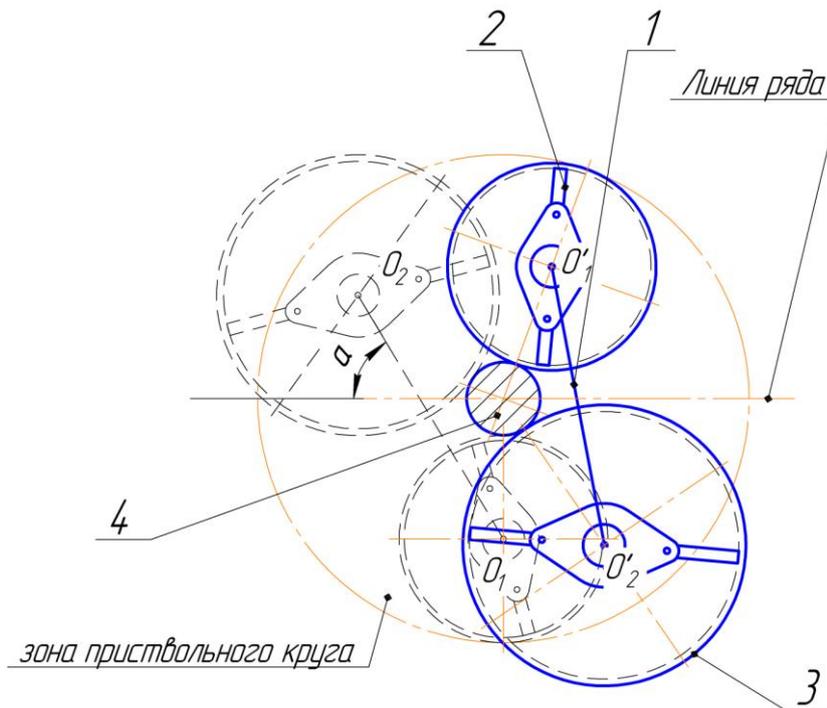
Конструктивная и технологическая схемы поворотного механизма косилки (Пат. РФ № 221758)
